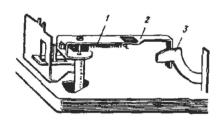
Механизм автостопа ЭПУ: 1 — пружина; 2 — подвижный рычаг, 3 — упор
